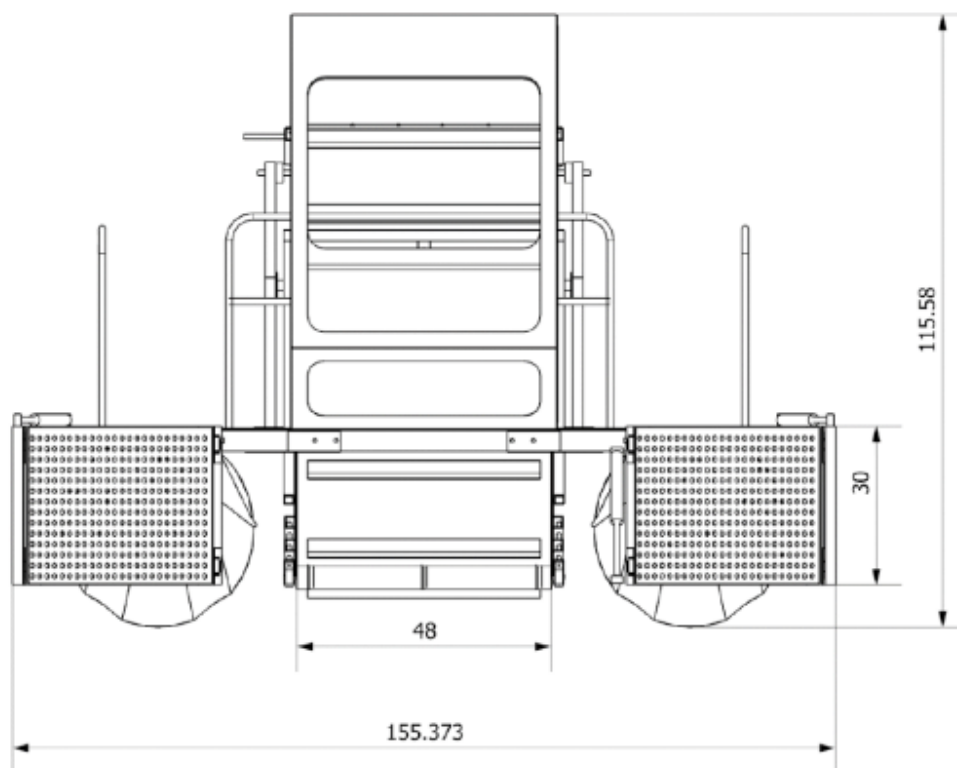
Dimensions del *Mobile Skimmer* (cm) (2)
